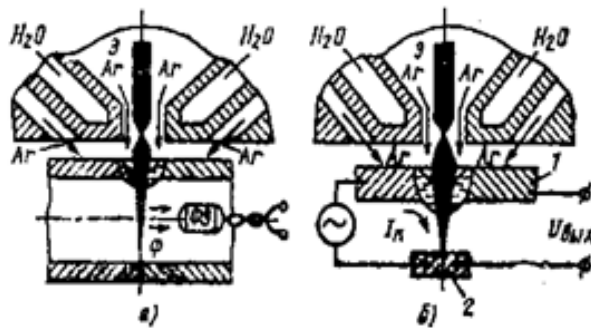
Способы контроля проплавления при плазменно-дуговой сварке
